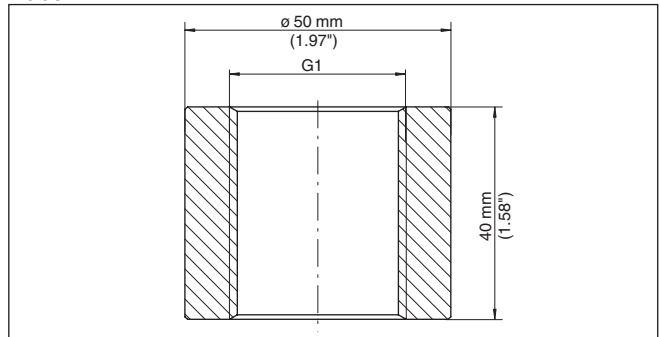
Maße Einschweißstutzen Gewinde G1 (DIN 3852-E) x 40 mm - VEGABAR 82
